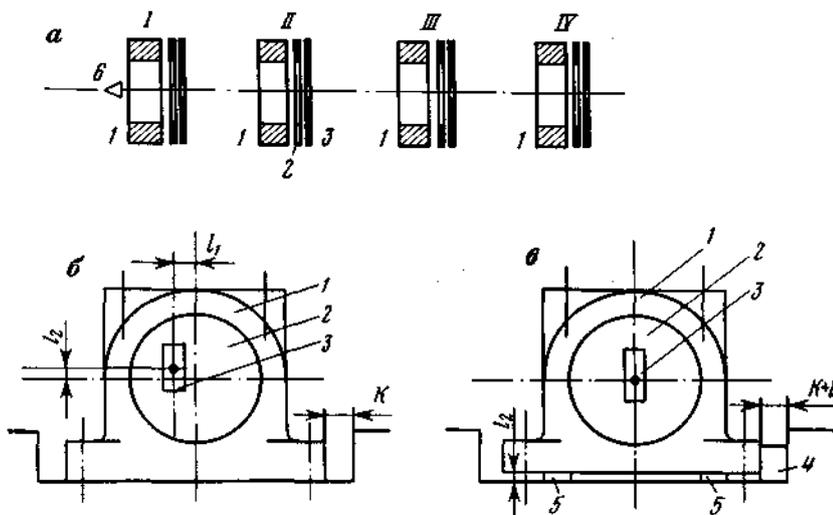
Схема проверки оборудования световым лучом «лазером»: а – схема центрирования: I – базовый подшипник, II, III, IV – центрируемые подшипники; б – положение мишени относительно центра отверстия при прохождении светового луча через все мишени (отверстия мишени и центр отверстия подшипника не совпадают); в – положение мишени относительно центра отверстия после центрирования (отверстие мишени совпадает с центром отверстия подшипника); 1 – подшипник, 2 – щиток, 3 – мишень, 4 – клин, 5 – подкладка, б – источник света (лазер) [31]
